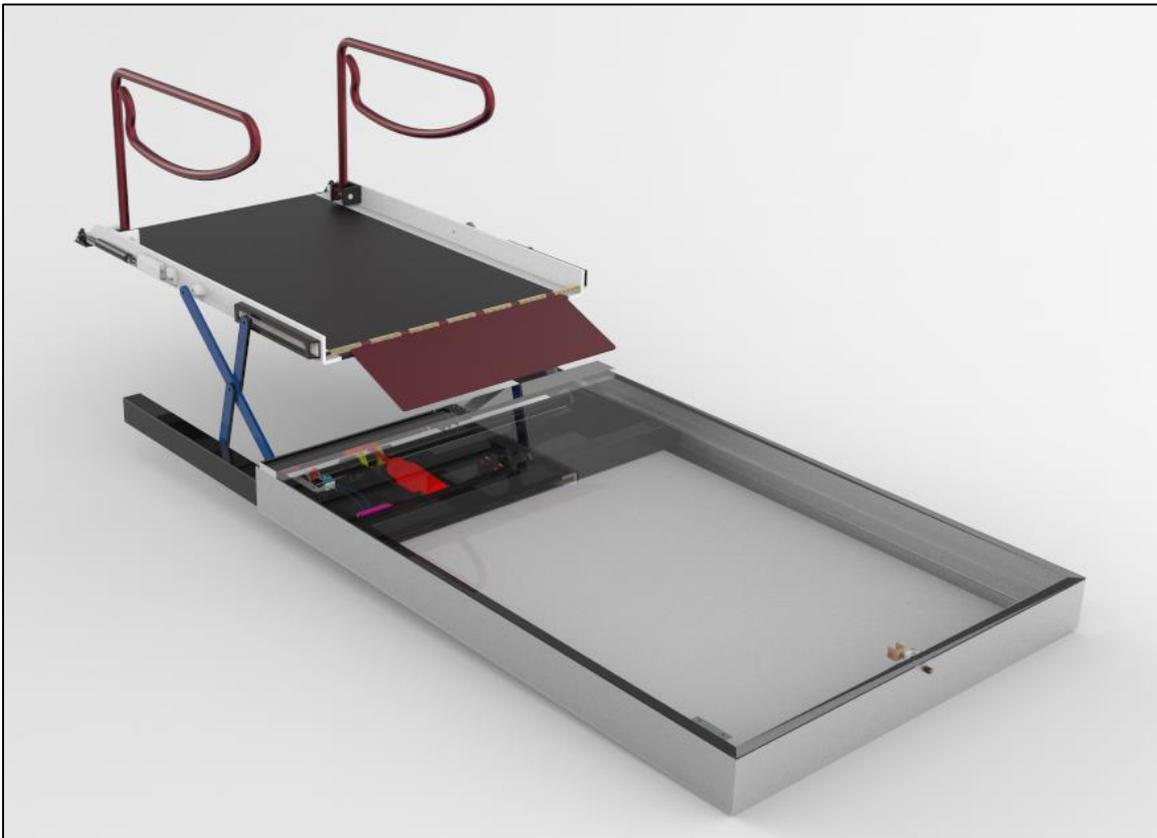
Vue isométrique de dessous de la plate-forme
